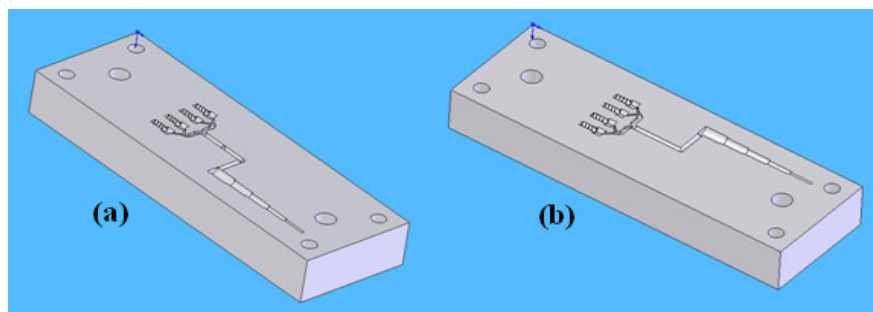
Projeto do molde do parafuso e componentes, face (a) e face (b).
